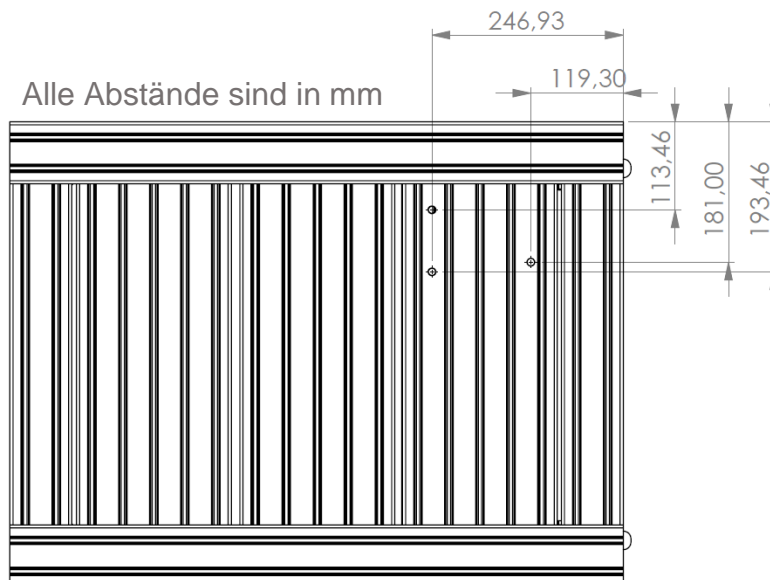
Die benötigten drei Bohrungen für Befestigungen ohne Nutensteine
